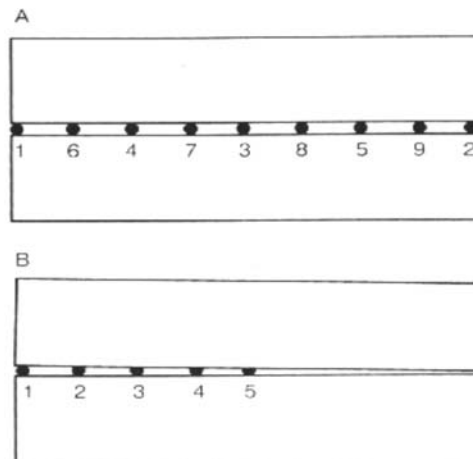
Técnica a utilizar para realizar la soldadura. Manual de soldadura y catálogo de productos. Empresa Oerlikon.
